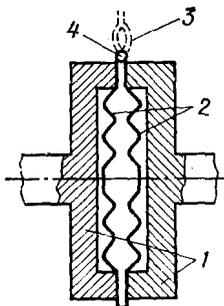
Схема аргонодуговой сварки мембраны:
